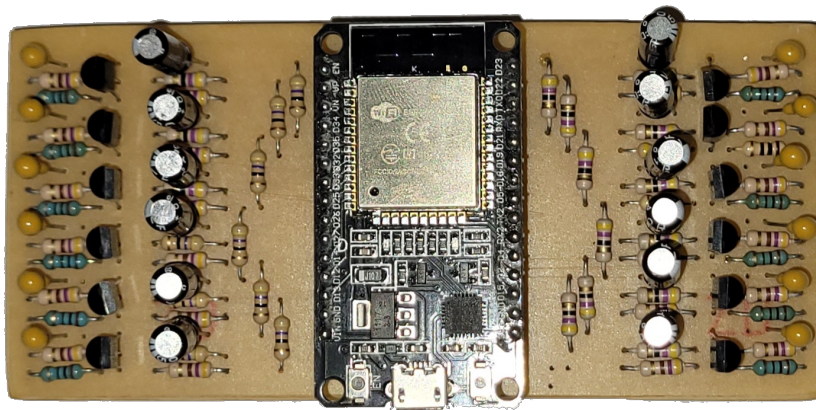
Módulo de Controle soldado na PCB
